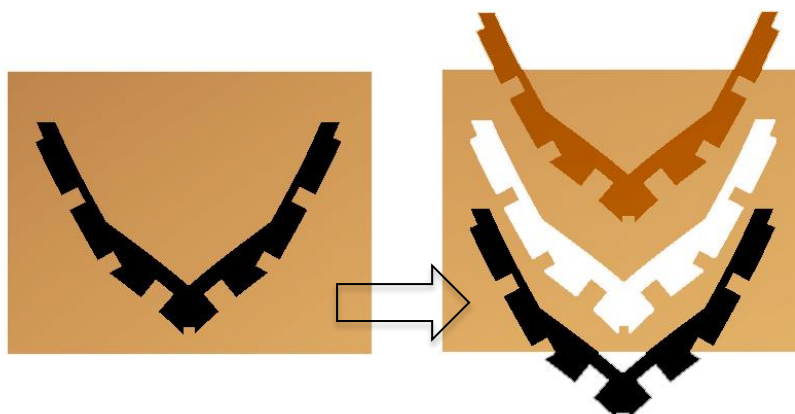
Imagen del proceso de corte de la pieza mediante la plantilla
